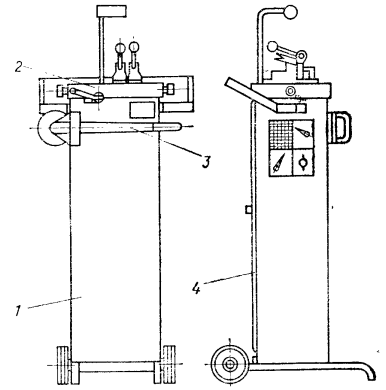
Машина типа МС-403 для стыковой сварки сопротивлением:
